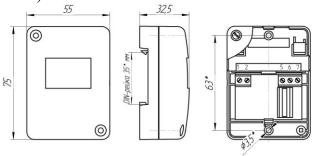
Габаритные и установочные размеры МАКС-УРП.
